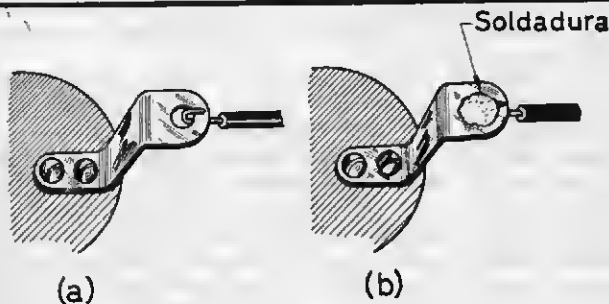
Soldadura sobre un terminal de conexión: (a) Antes de soldar se fija el extremo del hilo a la pieza de conexión; (b) Soldadura terminada.
